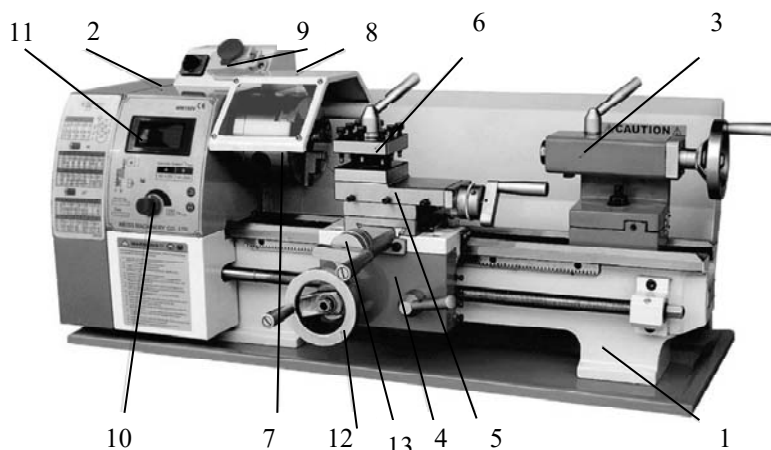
Общий вид токарного настольного станка Universal WM180V
